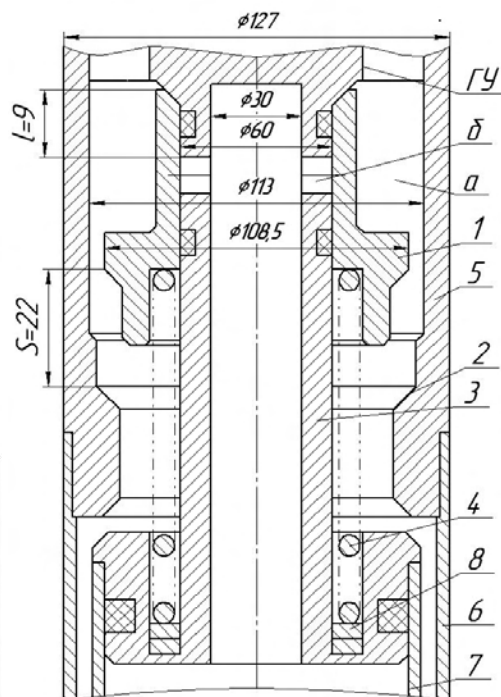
Схема НПУ с клапанно-золотниковым распределительным узлом: 1 – клапан-золотник; 2 – седло; 3 – распределительный шток; 4 – пружина; 5 – корпус; 6, 7 – наружная и внутренняя трубы колонкового набора; 8 – регулировочные кольца; а – камера НПУ; б – окна штока НПУ; ГУ – гидроударник
